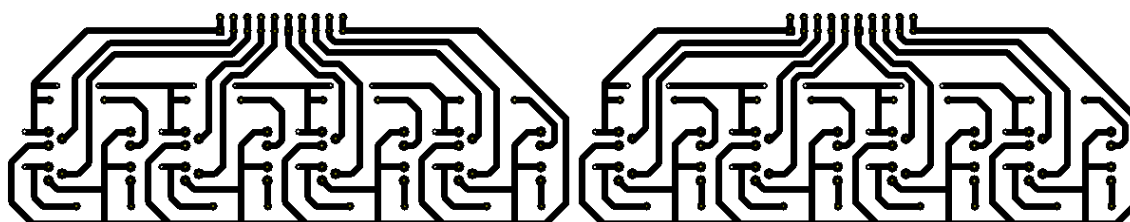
PCB Mòdul comptador d'abelles (Impressió Placa Baquelita)
